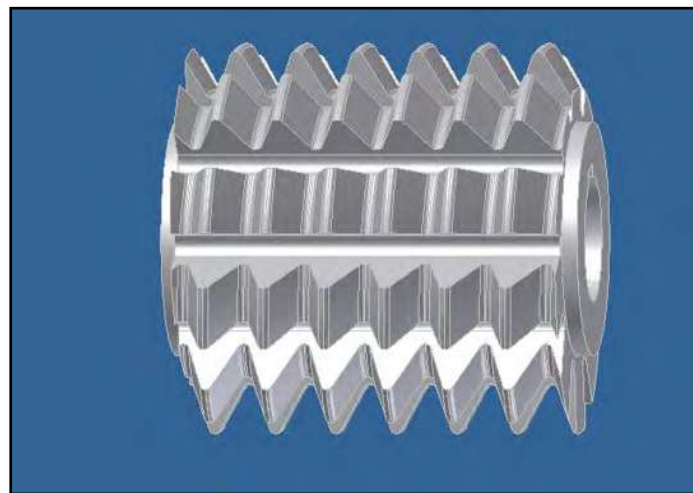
11. Diseño 2 de la fresa madre de módulo 5 mm.
